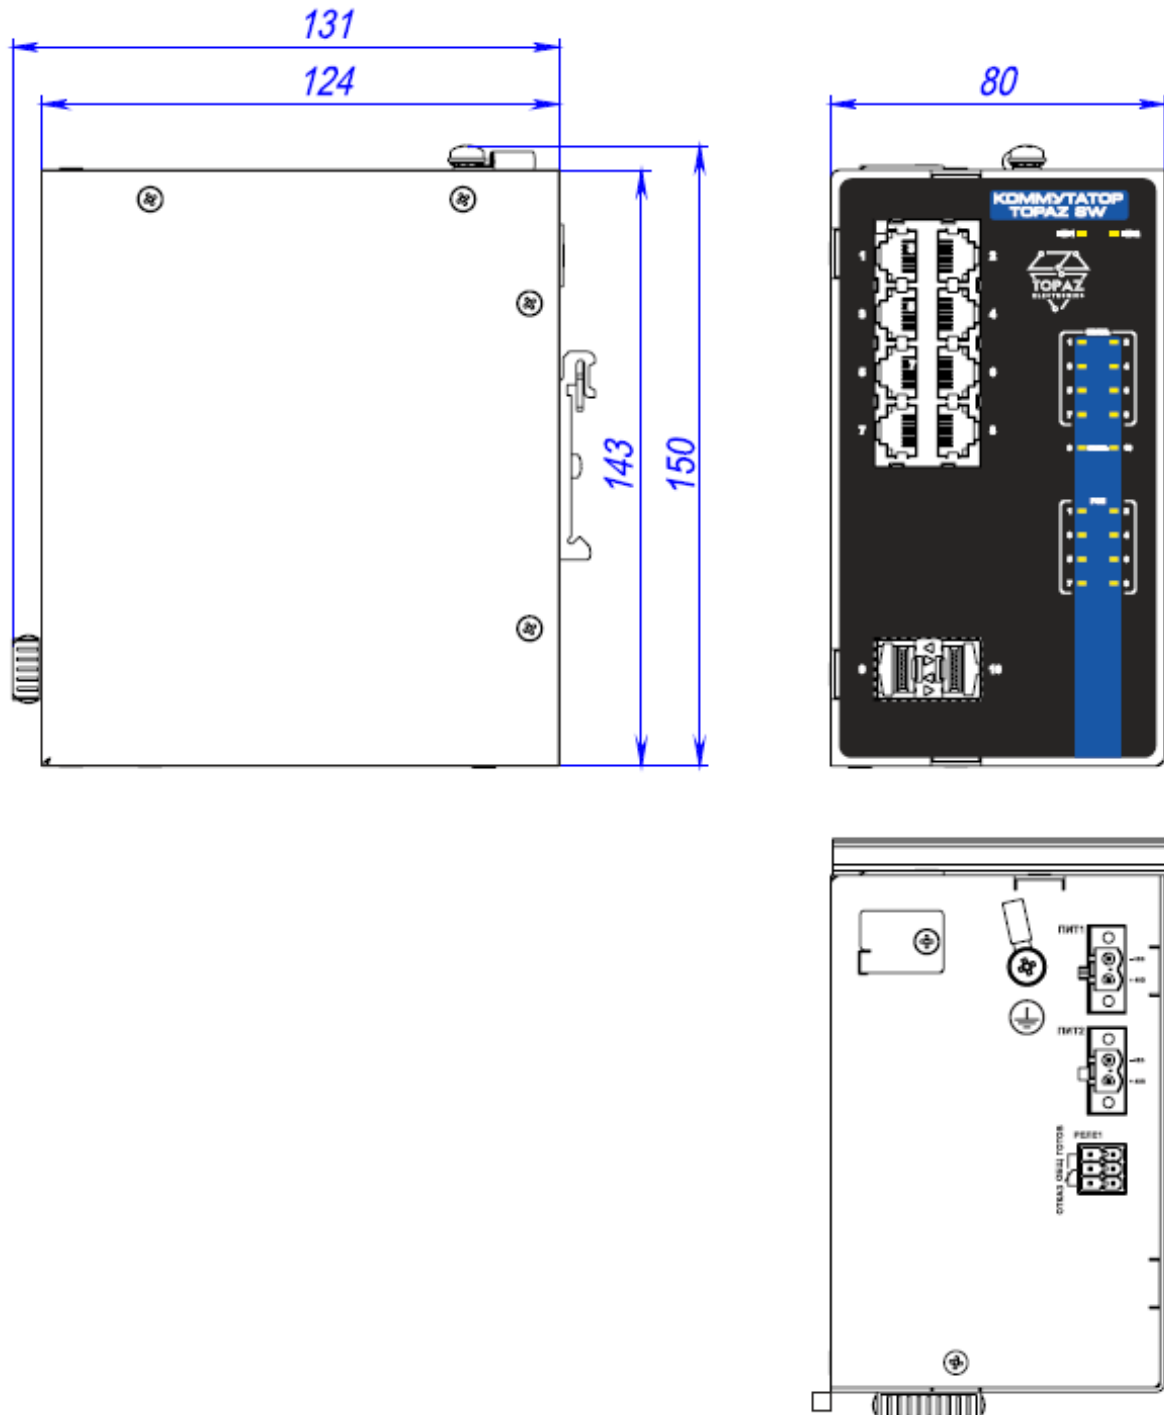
Внешний вид и габаритные размеры коммутатора
